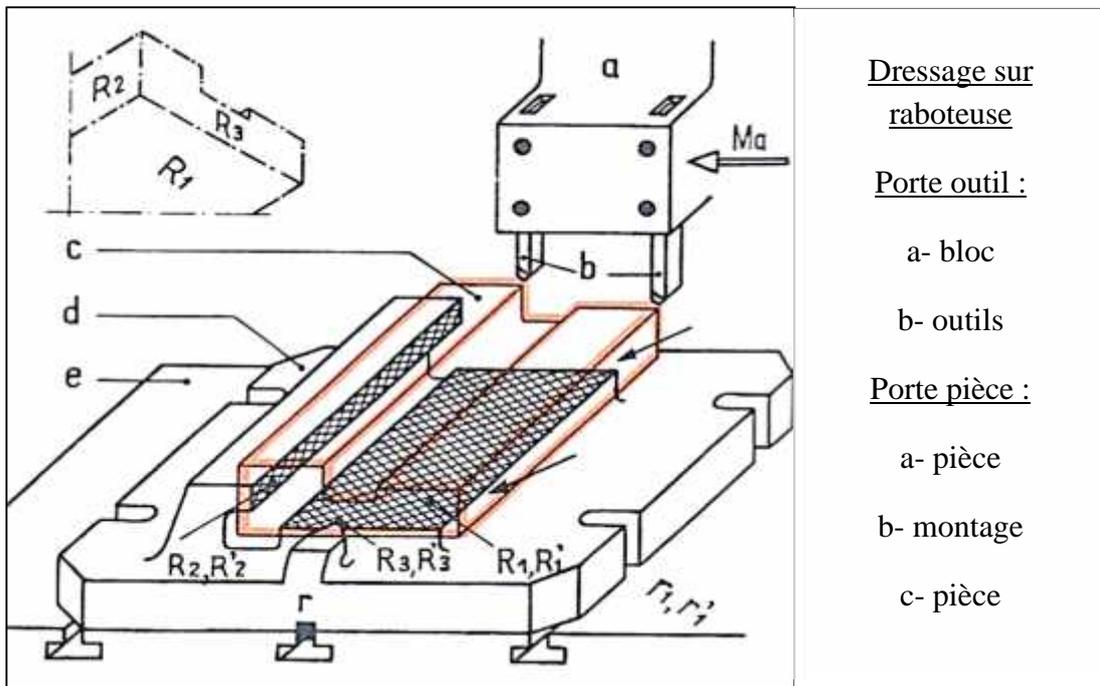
Usinage-type en montage (Dressage sur raboteuse) [CHE 82]
